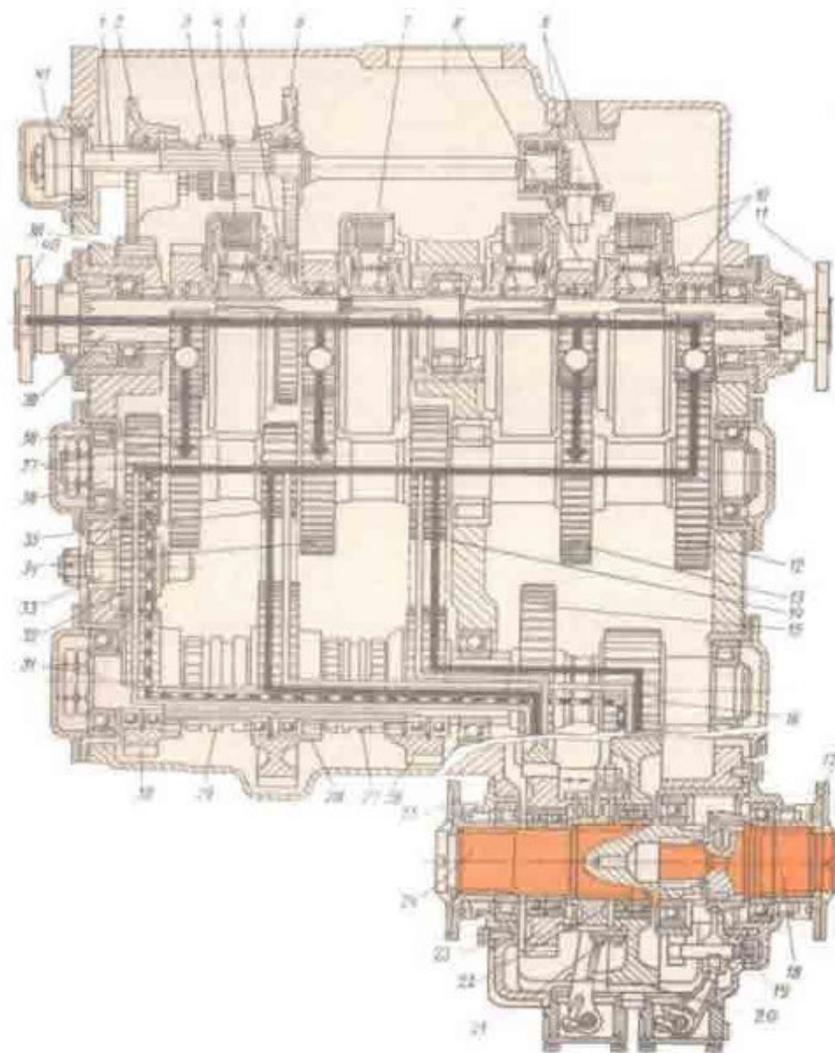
Схематический разрез коробки передач трактора К-700.
